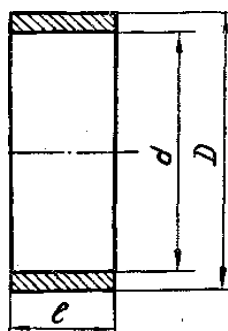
Эскиз заготовки с набором сменных установочных деталей. Интервал нагружения – 500 Н.
